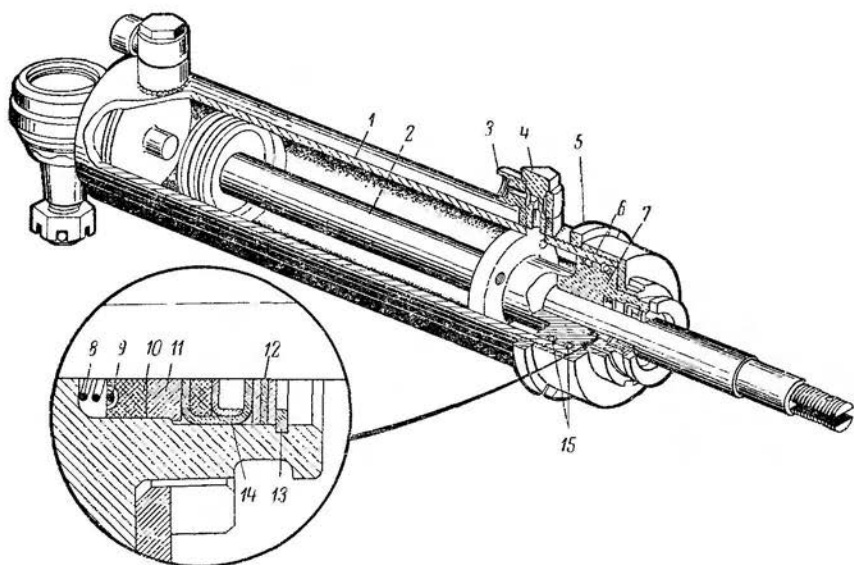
Силовой цилиндр гидроусилителя рулевого управления:
